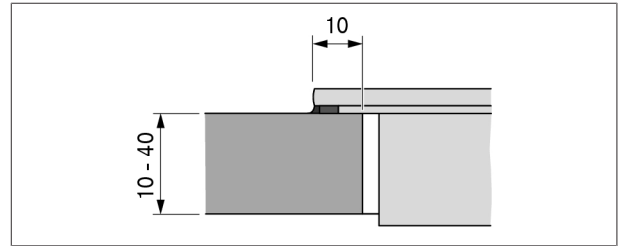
Rozmery drážky pre zapustenú montáž
